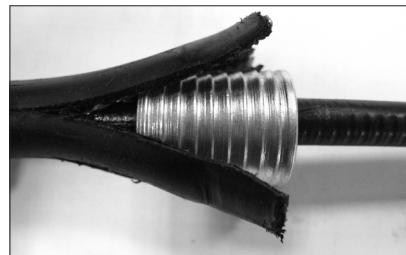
Установка конуса на ОК со сталеполиэтиленовой оболочкой
